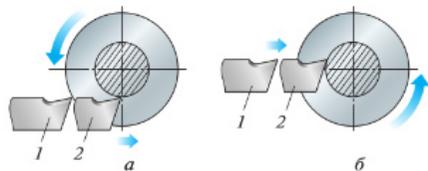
Положение отрезного резца в конце отрезания заготовки: *а* — при установке ниже центра; *б* — при установке выше центра (*1, 2* — положение резца)
